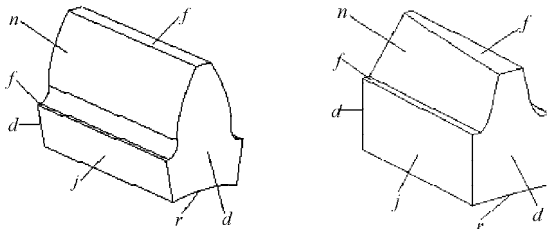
圆柱齿轮单齿边界条件 Fig. 1 Boundary conditions of single tooth of cylindrical gear
